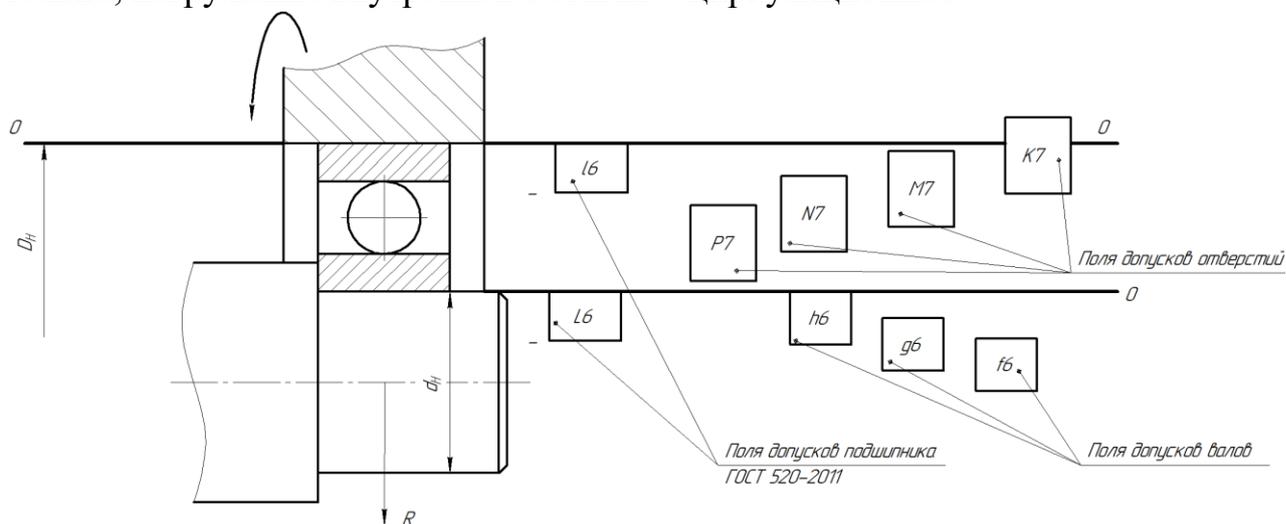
Схема полей допусков подшипника и сопряжённых деталей при вращающемся корпусе
